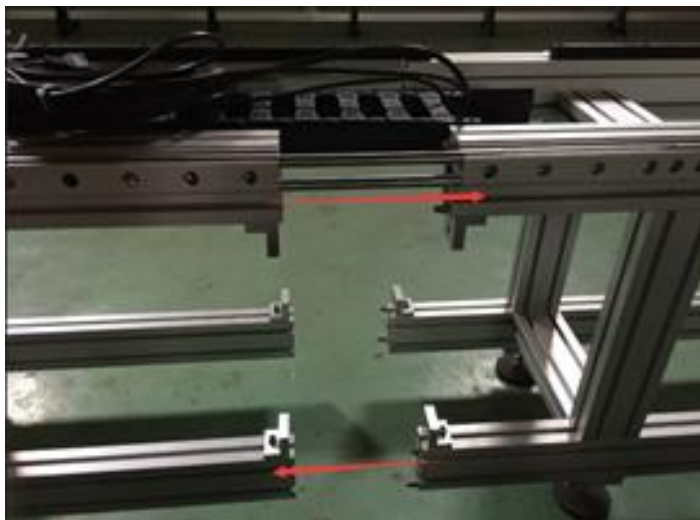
Стыковка секций 6-ти метрового станка (2500х6000)
